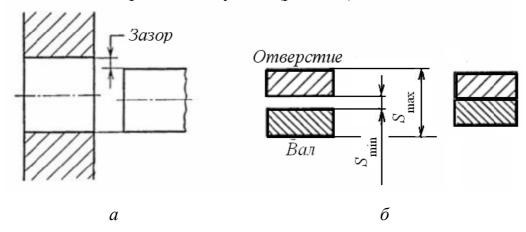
Посадка с зазором: a — общий вид соединения; δ — схема расположения интервалов допусков
